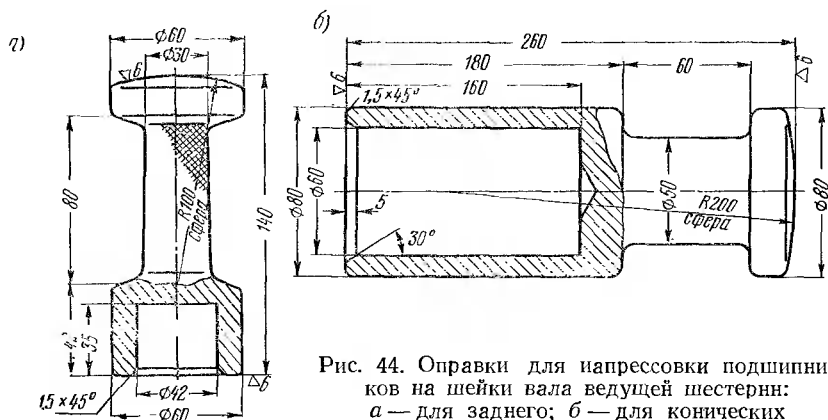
Оправки для напрессовки подшипников на шейки вала ведущей шестерни:
